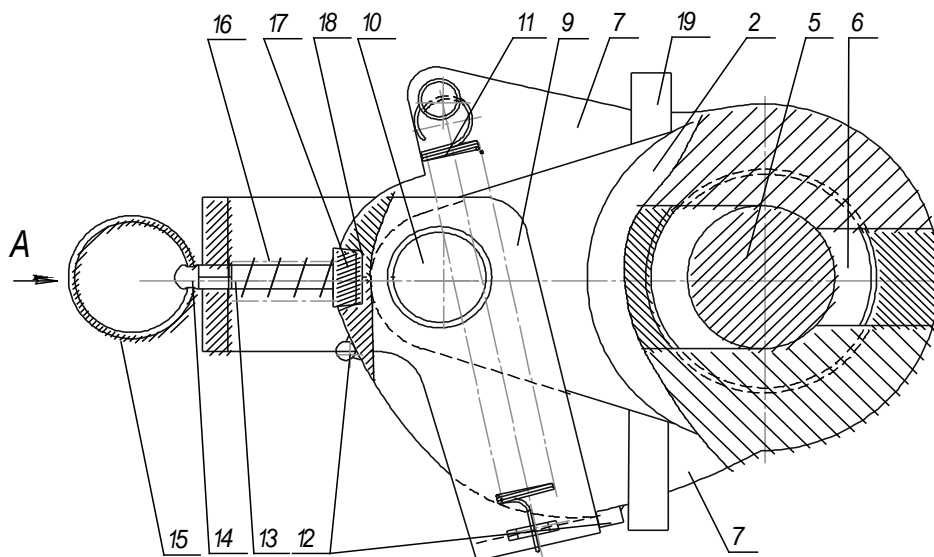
Вид сбоку на сцепное устройство тягача
